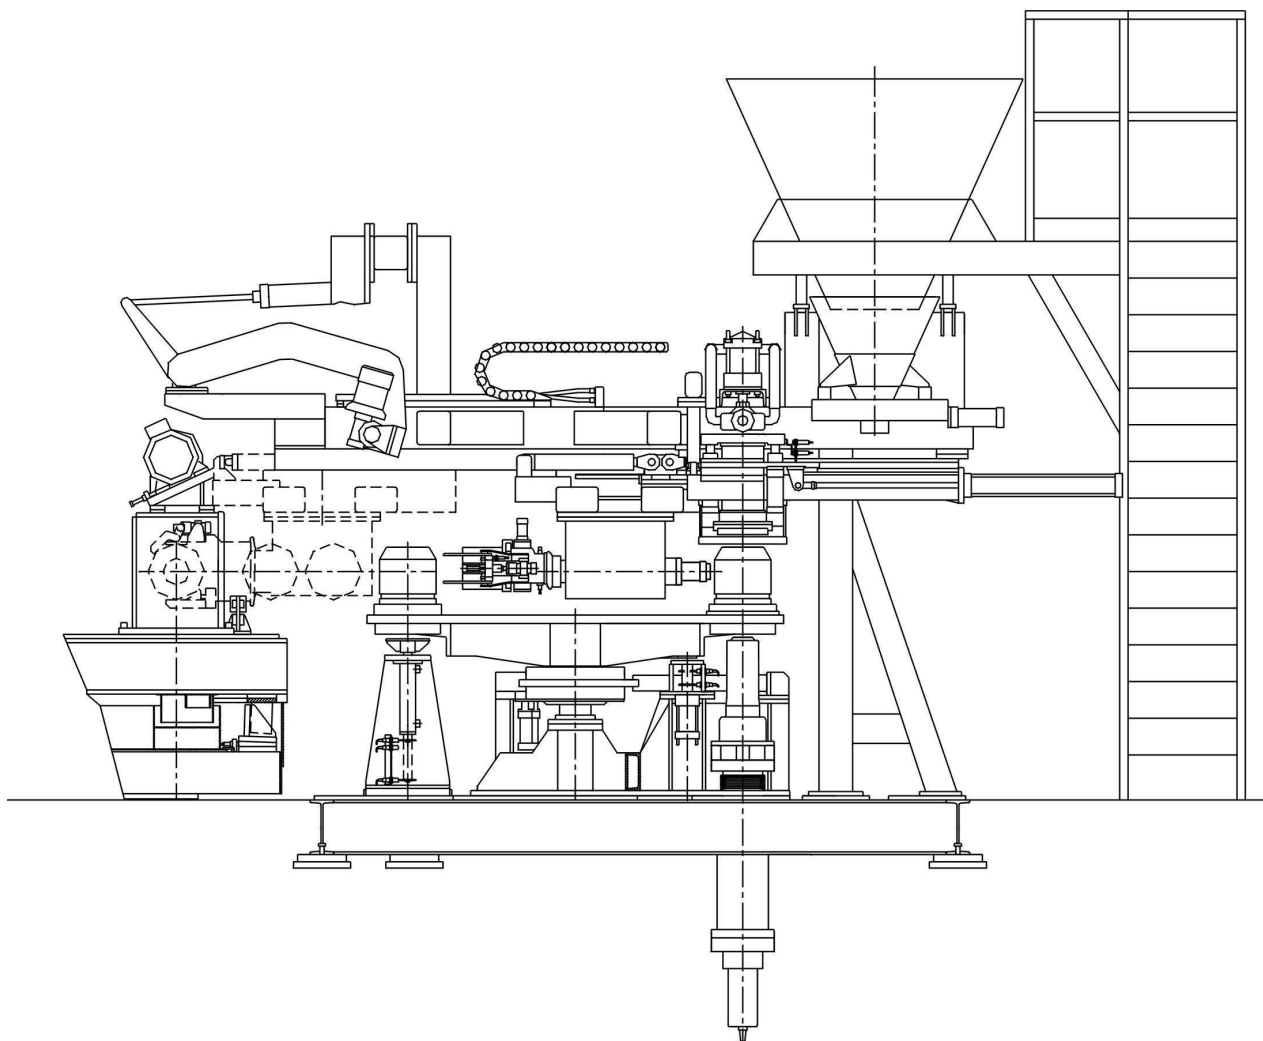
Wirówka do odśrodkowego odlewania tulei cylindrowych.
